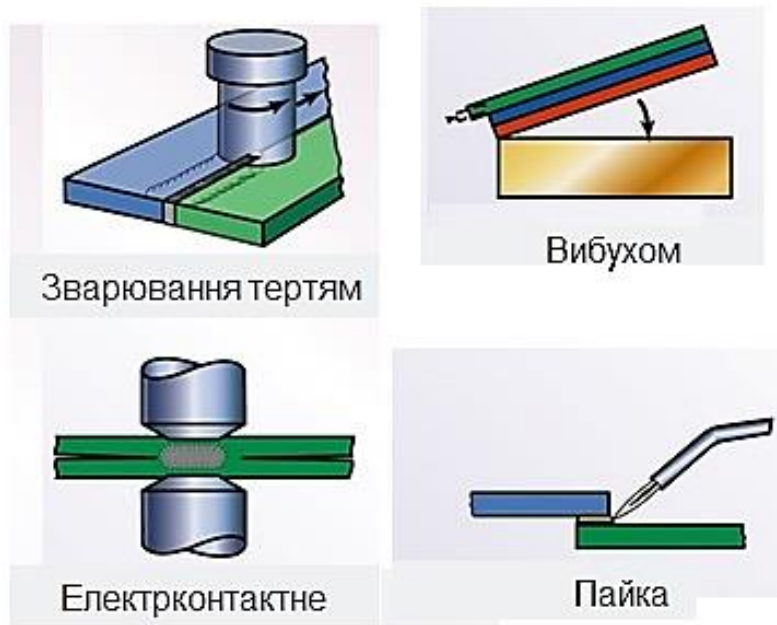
Деякі механічні, термомеханічні способи зварювання та пайка
